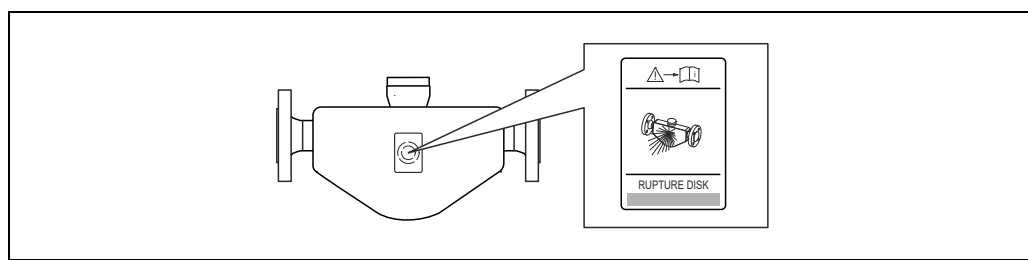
Дополнительный знак, указывающий расположение разрывного диска
